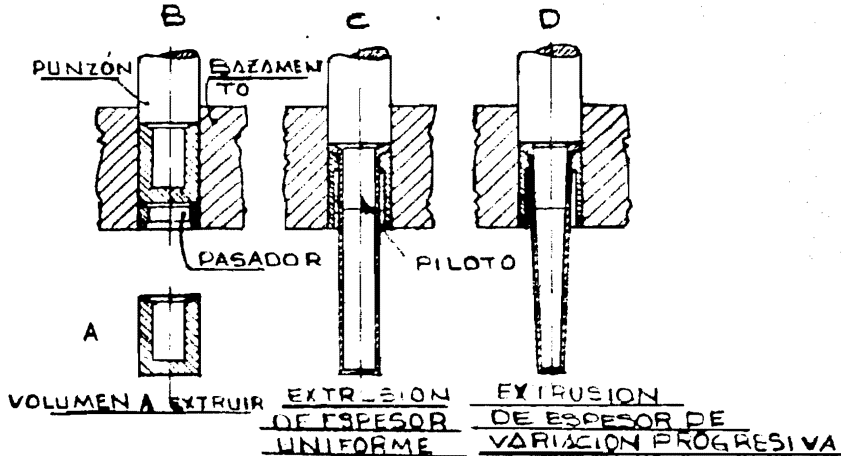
Representación esquemática del sistema de extrusión Hooker.
